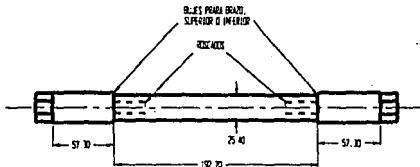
TUBO DE ALUMINICIO DE LOS RIELES PARA EL SOLDADO
